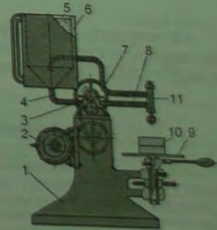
Схема установки для подготовки и запресовки модельного состава
